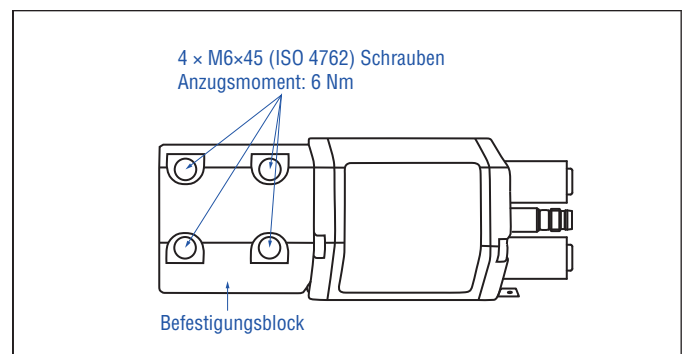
Befestigung des RDV Sensorelektronikgehäuses (Beispiel Bodenanschluss)
